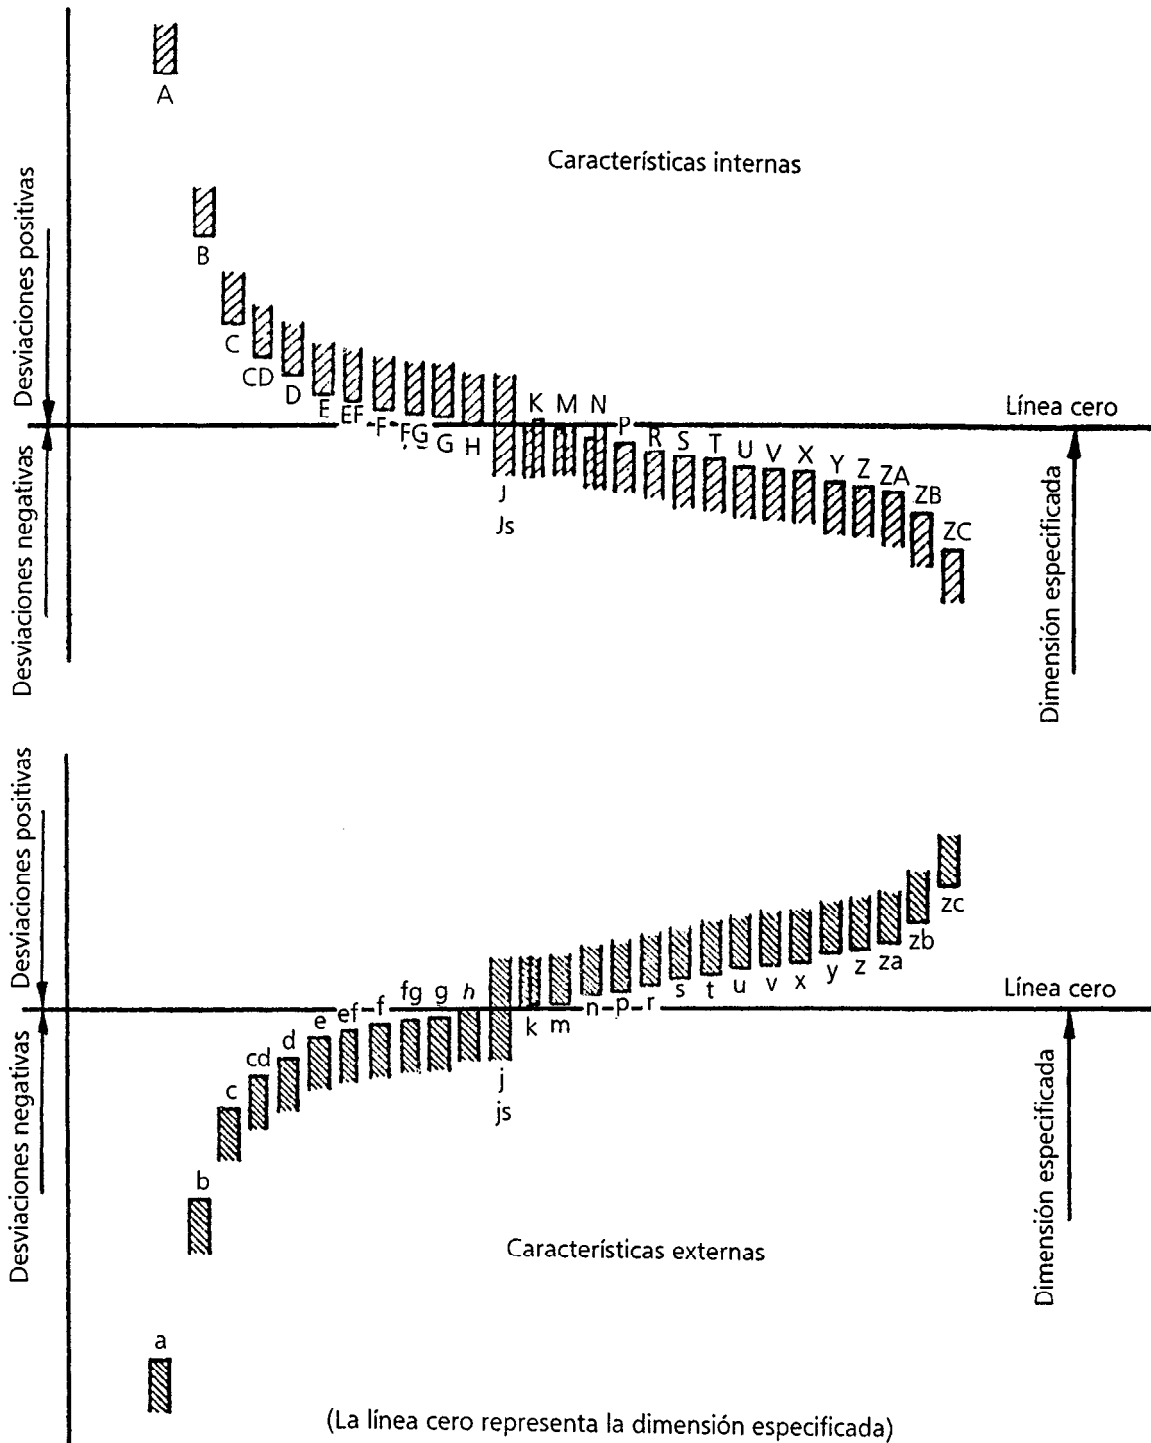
Posiciones respectivas de las diversas zonas de tolerancia para una dimensión dada.
